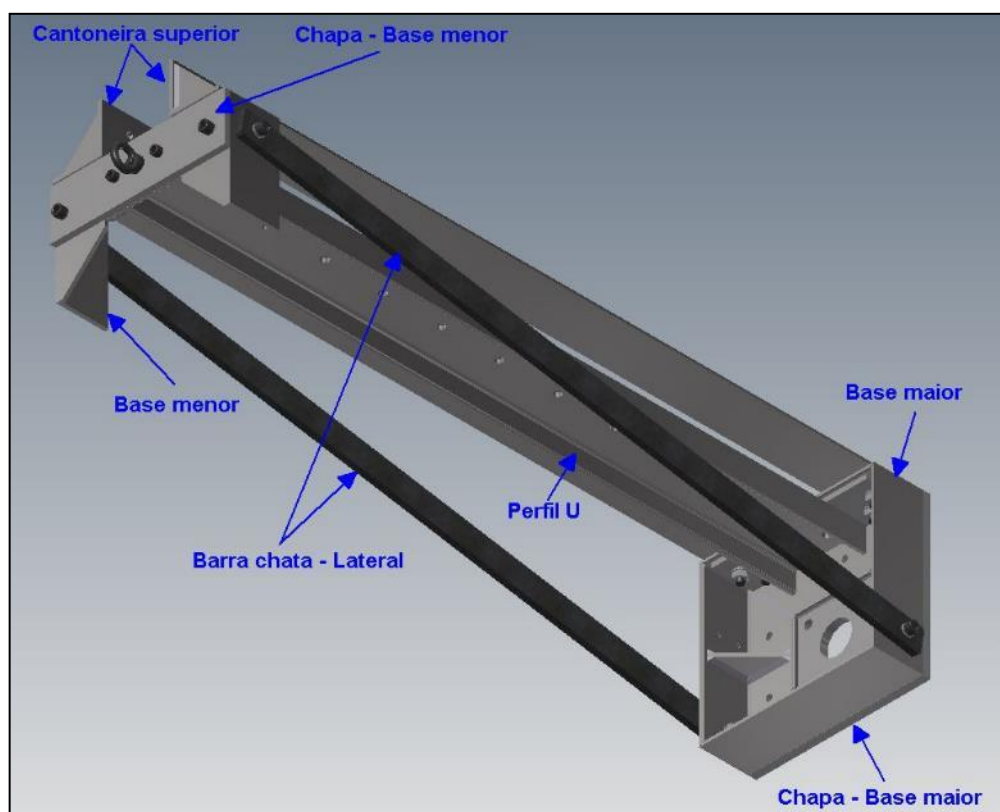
Projeto da estrutura do sistema de Tração da mísula
